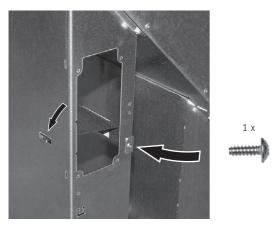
Inserire la linguetta nella cavità e fissare sul davanti con una vite autofilettante – vista da davanti
